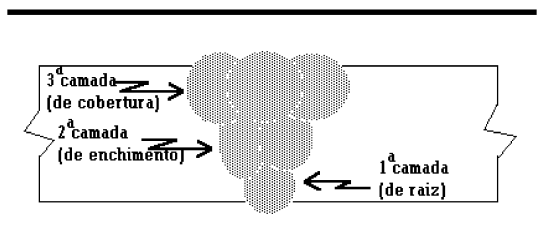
Seção Transversal de uma Junta Soldada, mostrando 6 “passes” em 3 camadas.
